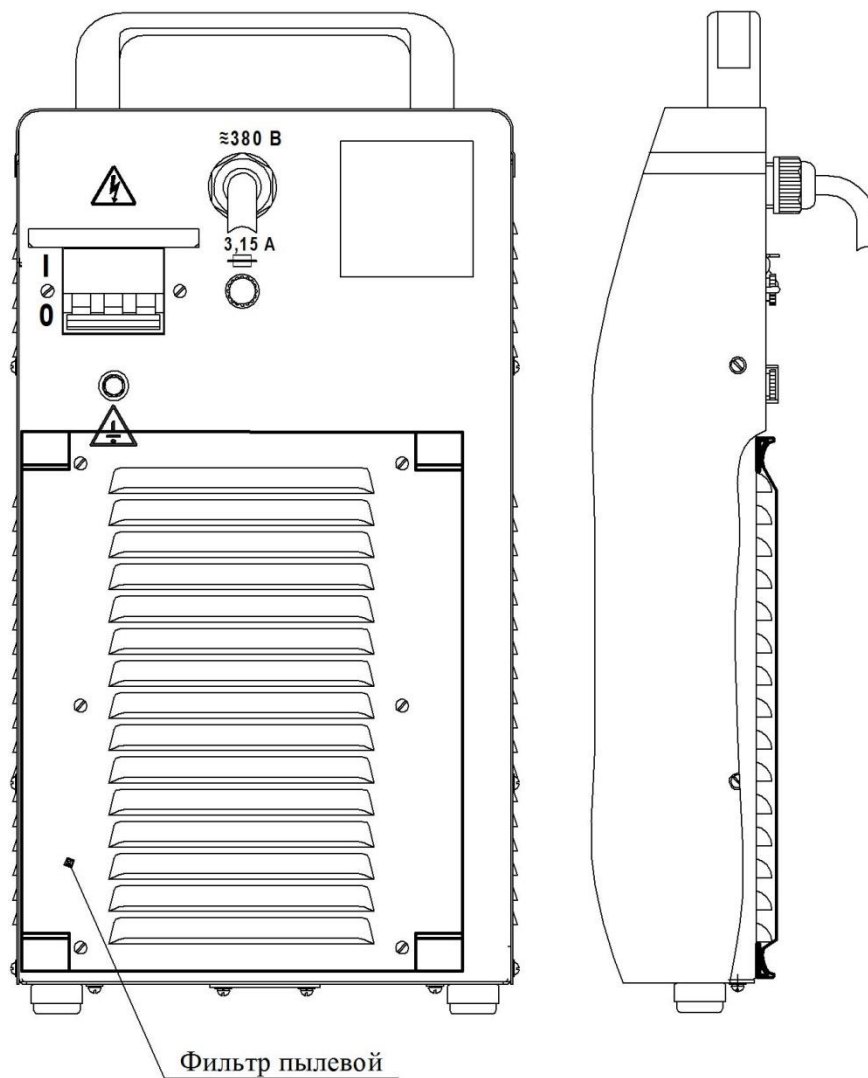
Источник питания инверторный специальный для дуговой сварки ДС400.33М
